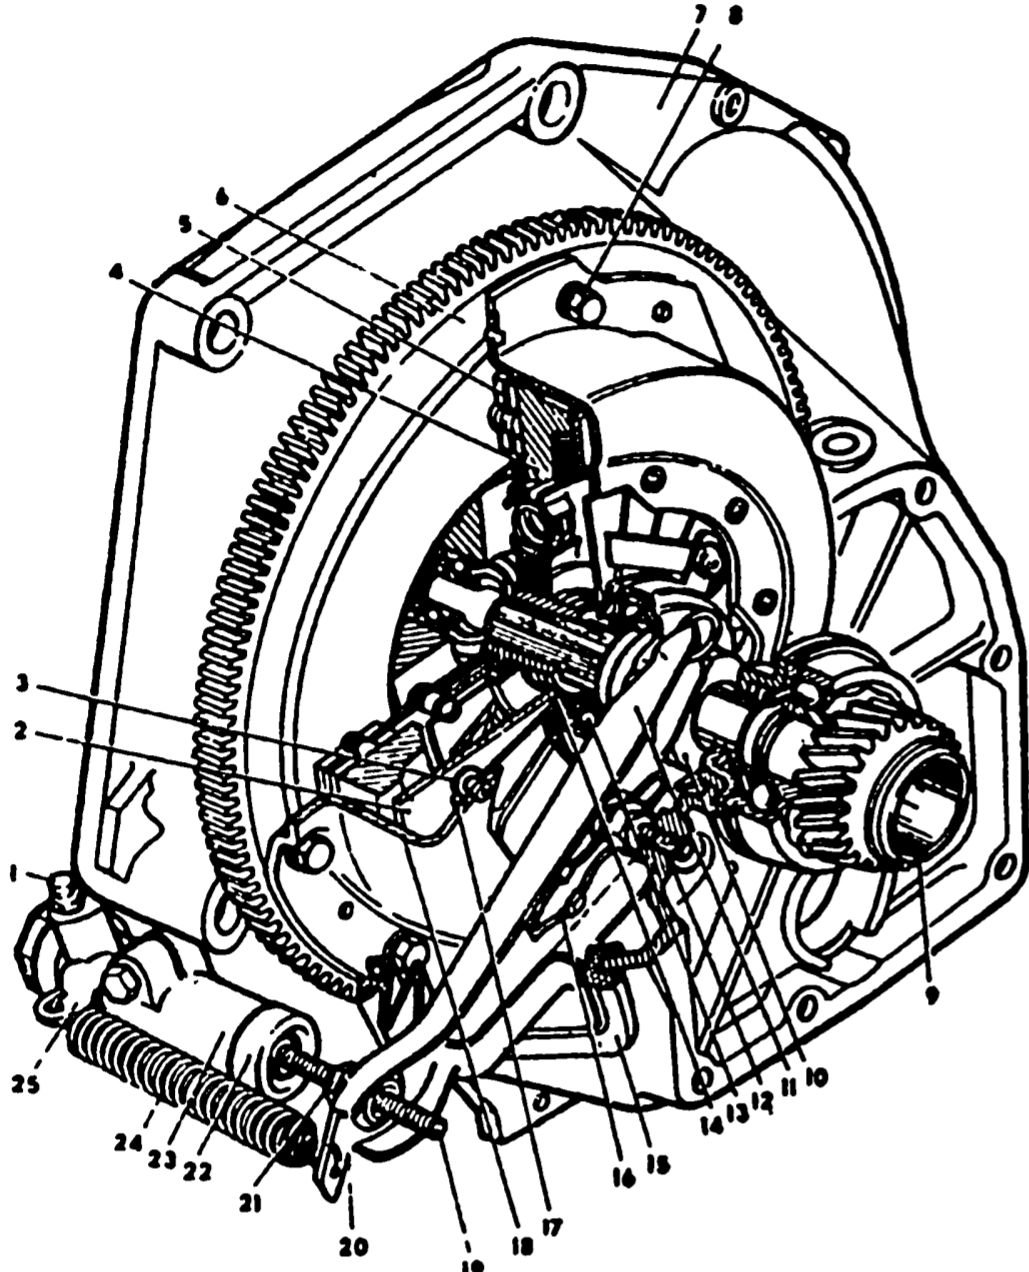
Сцепление в сборе: 1 - штуцер для прокачки; 2 - нажимная пружина сцепления; 3 - ступенчатая заклепка нажимной пружины; 4 - нажимной диск; 5 - ведомый диск; 6 - маховик; 7 - картер сцепления; 8 - болт крепления кожуха сцепления к маховику; 9 - первичный вал коробки передач; 10 - муфта подшипника выключения сцепления; 11 - вилка выключения сцепления; 12 - шаровая опора вилки выключения сцепления; 13 - подшипник выключения сцепления; 14 - упорный фланец нажимной пружины; 15 - чехол вилки выключения сцепления; 16 - пружина вилки выключения сцепления; 17 - опорное кольцо нажимной пружины; 18 - кожух сцепления; 19 - толкатель вилки выключения сцепления; 20 - регулировочная гайка; 21 - контргайка; 22 - защитный колпачок цилиндра привода выключения сцепления; 23 - цилиндр привода выключения сцепления (рабочий цилиндр); 24 - оттяжная пружина вилки; 25 - скоба оттяжной пружины
